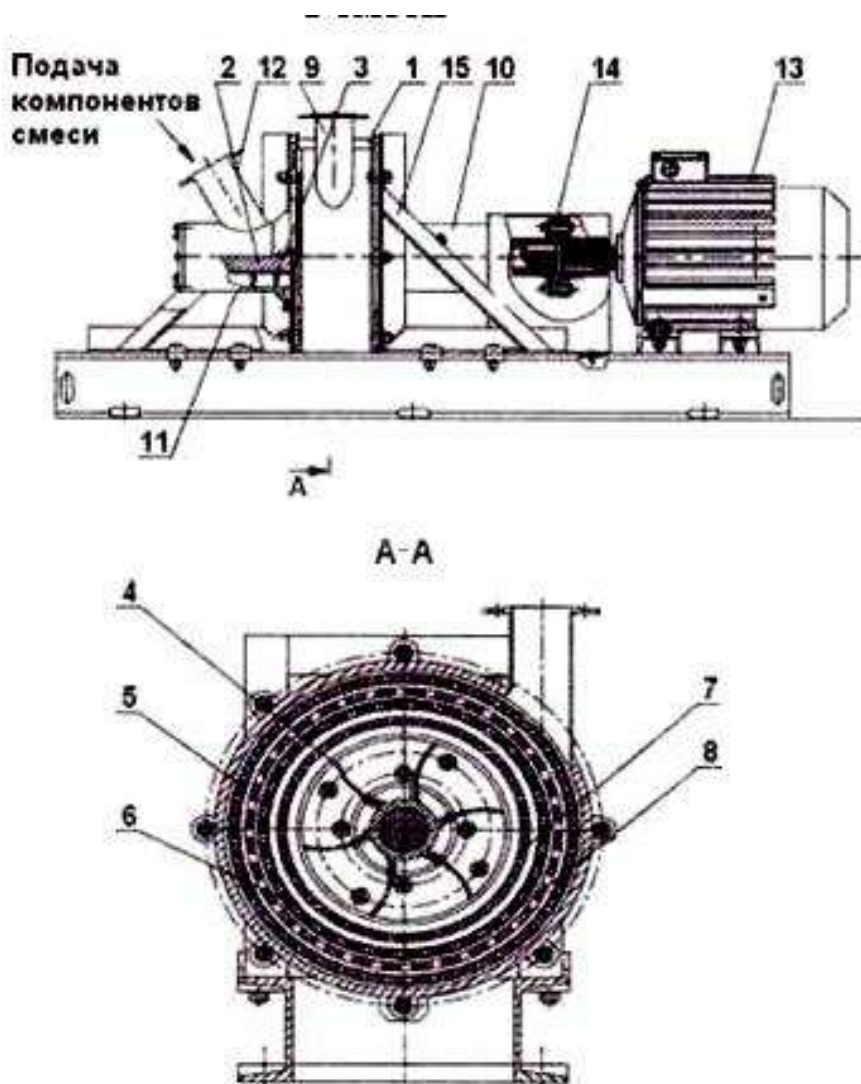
Схема РПА проточного типа: 1 – приводной вал; 2 – ротор; 3 – патрубок выхода суспензии; 4 – крышка-статор; 5 – патрубок входа
